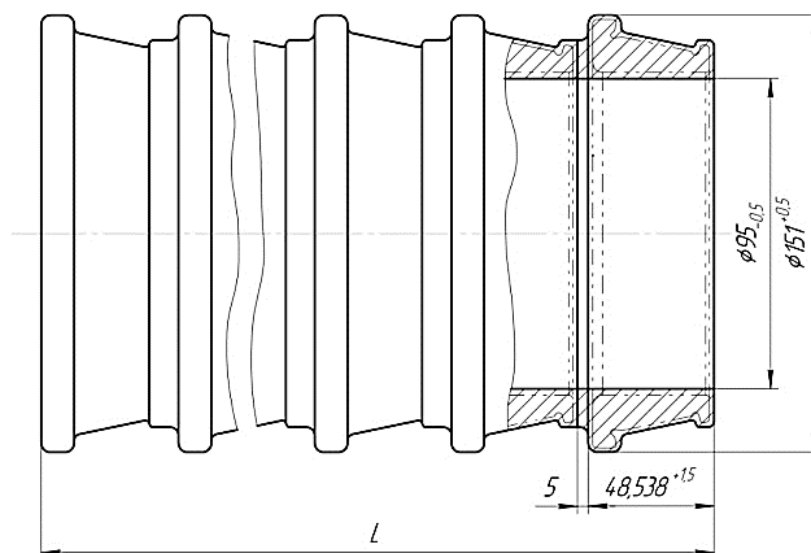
Вид трубной заготовки с РПП для механической обработки внутреннего кольца роликоподшипника
